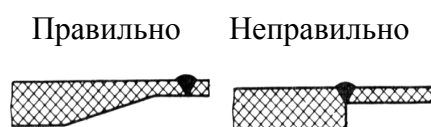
Подготовка материалов различной толщины при сварке их горячим воздухом
